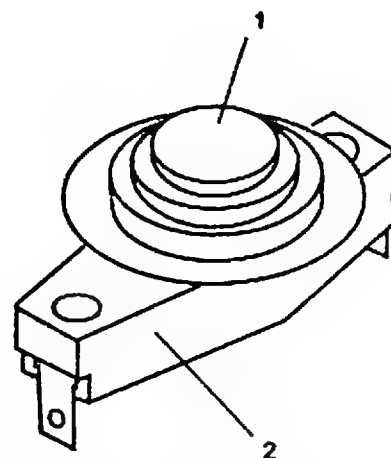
Общий вид биметаллического термостата: 1 — датчик; 2 — корпус
